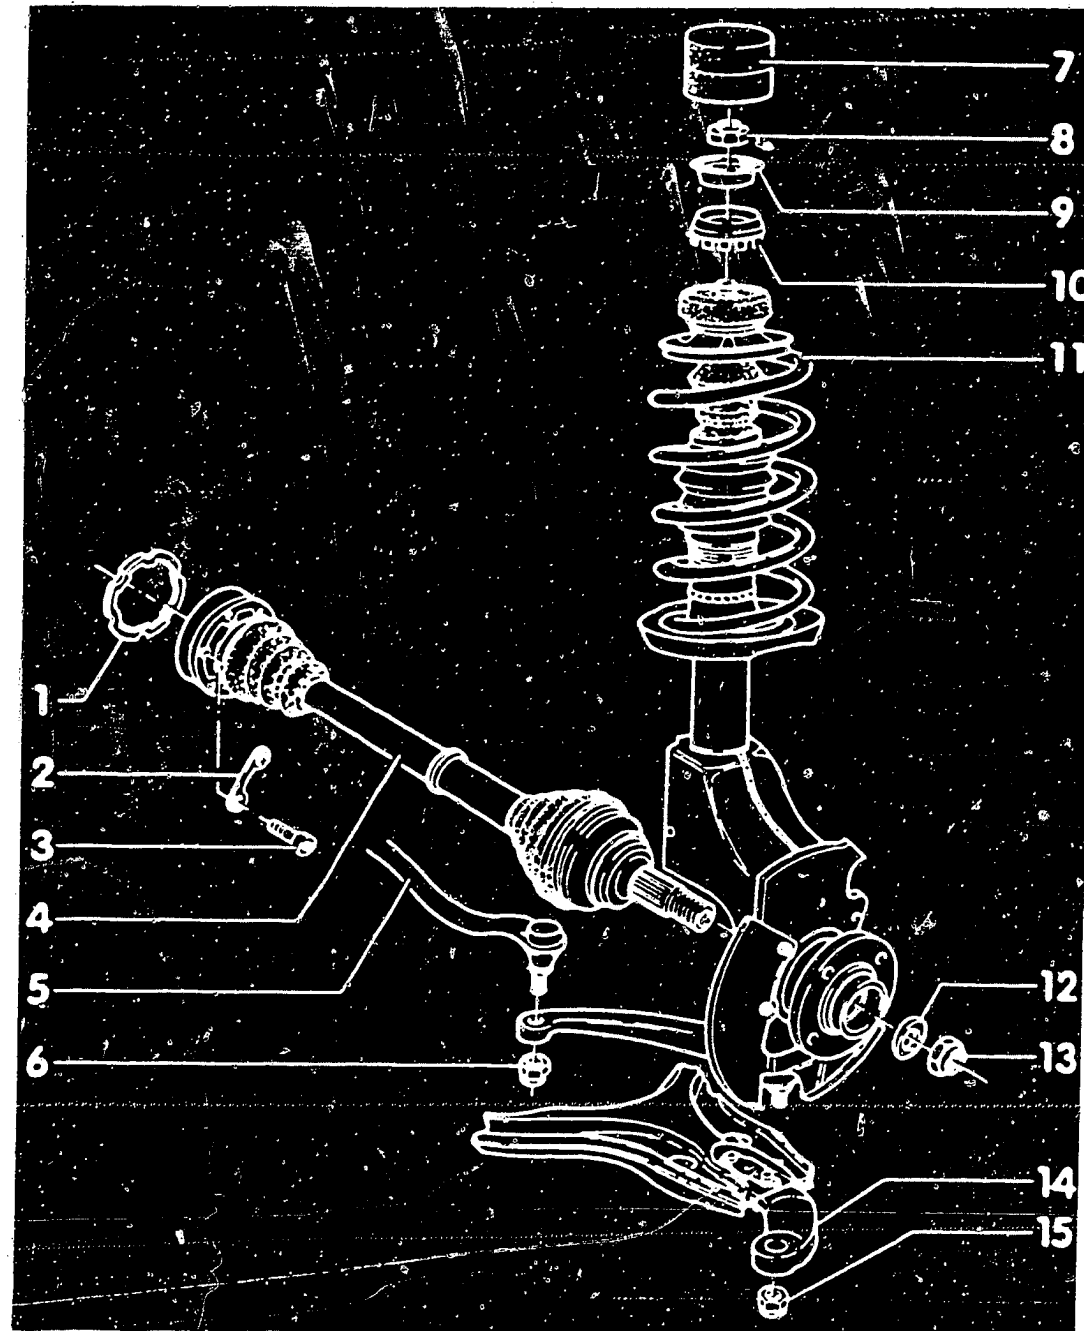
Vorderradaufhängung in ihre Einzelteile zerlegt. 1 Führungsring – 2 Sicherung – 3 Schraube – 4 Gelenkwelle – 5 Spurstange – 6 Spurstangengelenkmutter – 7 Kappe – 8 Mutter – 9 Topfscheibe – 10 Blechring – 11 Schraubenfeder – 12 Scheibe – 13 Radnabenmutter – 14 Unterer Querlenker – 15 Gelenkmutter.
